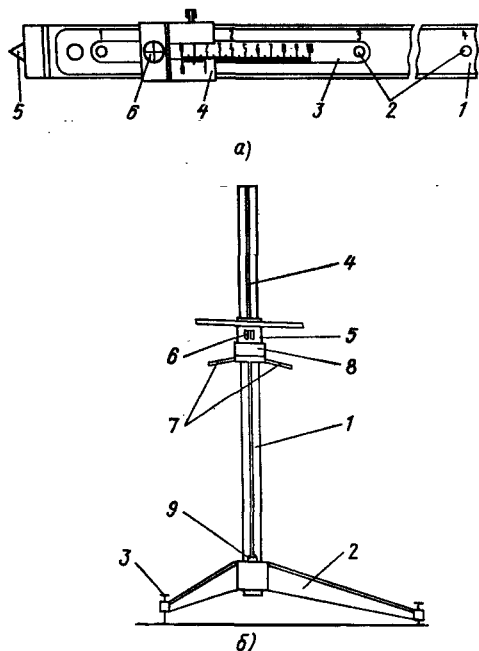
Специальные измерительные приспособления для лазерных устройств: а – линейка координатная; 1 – корпус; 2 – отверстие координатное; 3 – калибр; 4 – нониус; 5 – наконечник; 6 – марка; б – стойка измерительная; 2 – основание; 3 – подъемный винт; 4 – шкала; 5 – каретка; 6 – нониус; 7 – рукоятка; 8 – гайка механизма перемещения каретки; 9 – сферический уровень
